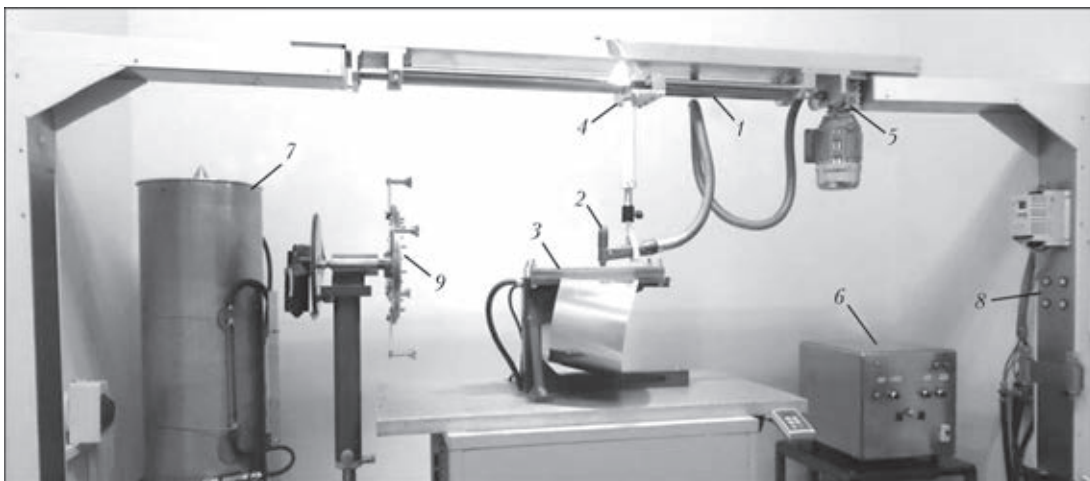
Экспериментальный стенд для сварки заготовок преобразуемых оболочек из фольговых материалов: 1 — механизм перемещения; 2 — плазматрон; 3 — сборочно-сварочная оснастка с конической заготовкой оболочки КПО; 4 — каретка механизма перемещения; 5 — двигатель с редуктором; 6 — источник питания микроплазменной сварки; 7 — теплообменный модуль плазматрона; 8 — автоматическая система позиционного регулирования параметров сварочного процесса; 9 — приспособление для сварки кольцевых швов КПО
